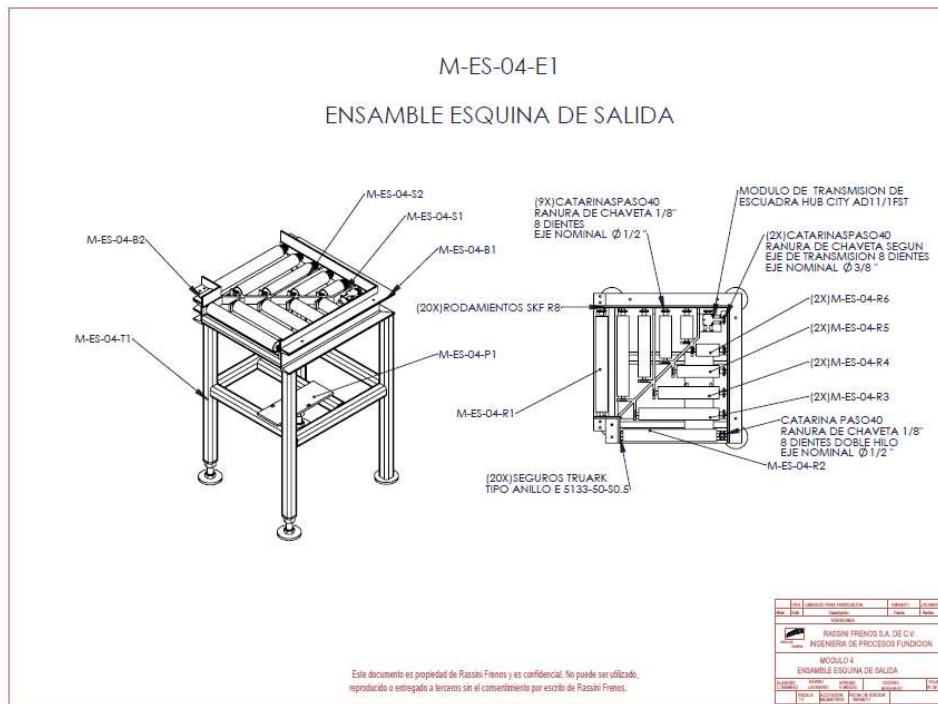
Plano de fabricación ensamble final de esquina de salida
